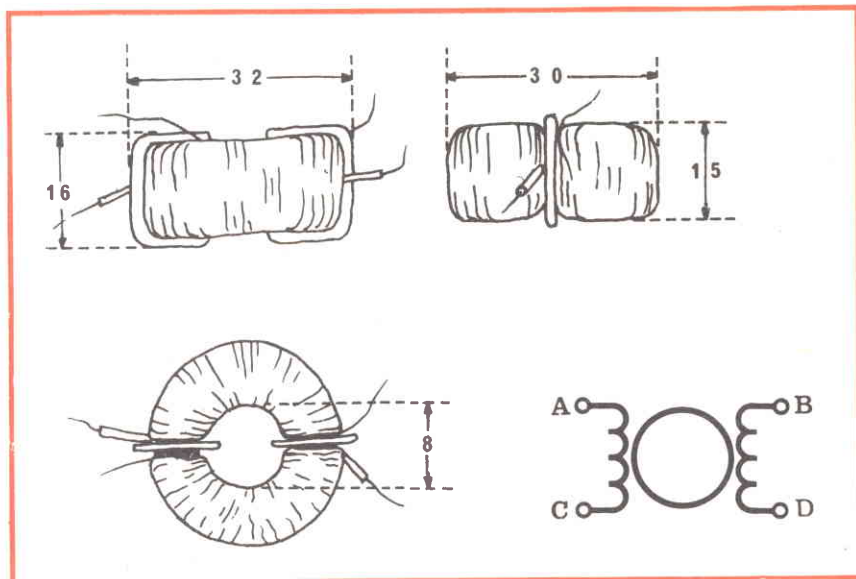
Disegno e schema elettrico del toroide. Le dimensioni sono espresse in millimetri.
